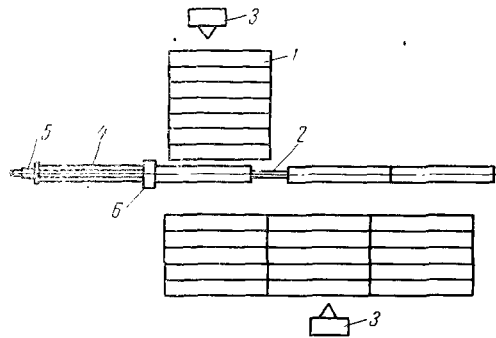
Схема стационарной установки для стыковой электроконтактной сварки труб в секции (ТКУС)
